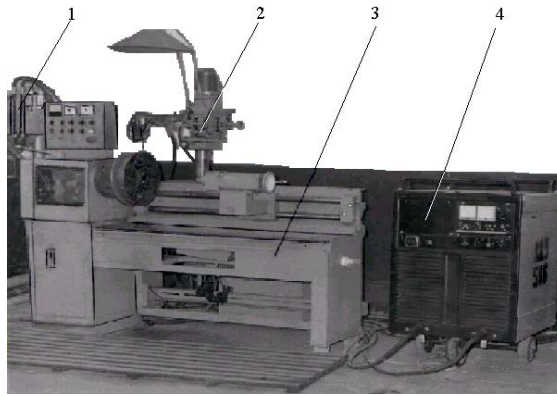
Загальний вигляд установки для наплавлення деталей з газополуменевим захистом зварювальної ванни. 1 – газорозподільча апаратура; 2 – подаючий механізм із газоелектричним пальником; 3 – наплавлювальна установка УД-209; 4 – джерело струму ВДУ-506.
